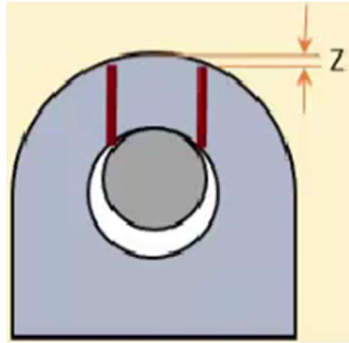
Fallo por corte a lo largo de dos planos (Engineering Solved, 2016)
